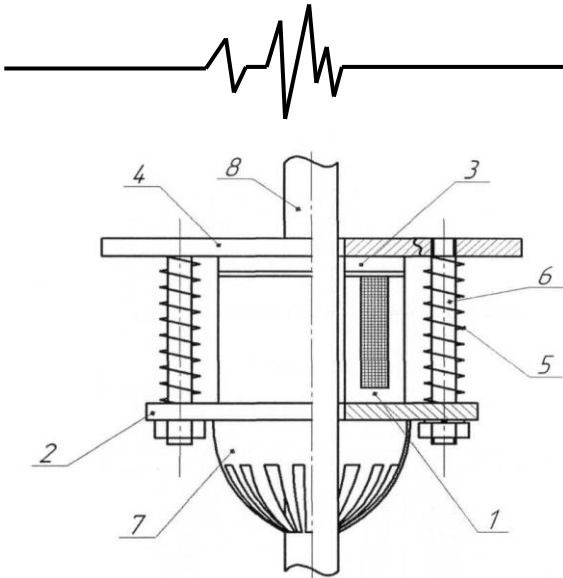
Вібраційний пересувний пристрій: 1, 3 – статор і яркір електромагнітного вібропривода; 2 – основа; 4 – платформа; 5 – циліндрична пружина; 6 – напрямна; 7 – стопорний механізм; 8 – вертикальна циліндрична поверхня (колона)
